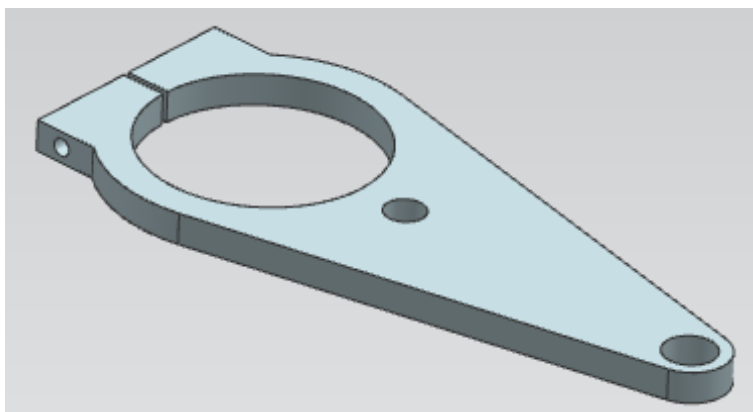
CAD Modell eines Hebels für die Ausführung ohne Biegeelenker
